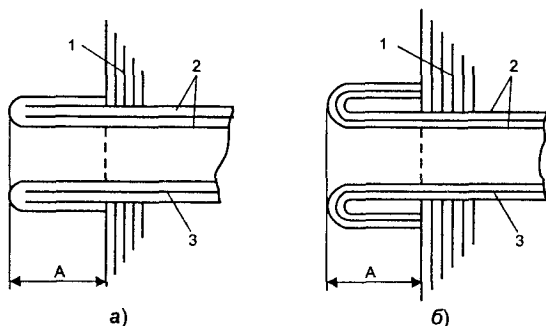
Расположение пазовой коробочки в пазу и вылет манжеты: а — манжета, образованная внутренним слоем пазовой коробочки, б — манжета, образованная тремя слоями пазовой коробочки; 1 — пакет железа, 2 — электрокартон, 3 — внутренний слой лакоткани или миканита
